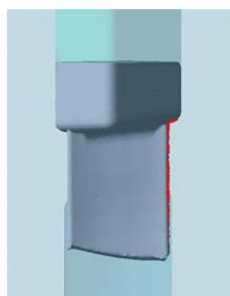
Змодельована в QForm заготовка компресорної лопатки, отримана методом видавлювання
